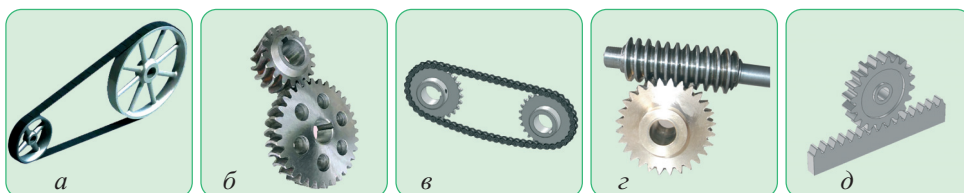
Передаточные механизмы: а – ременная передача; б – зубная передача; в – цепная передача; г – винтовая передача; д – зубчатореечная передача
